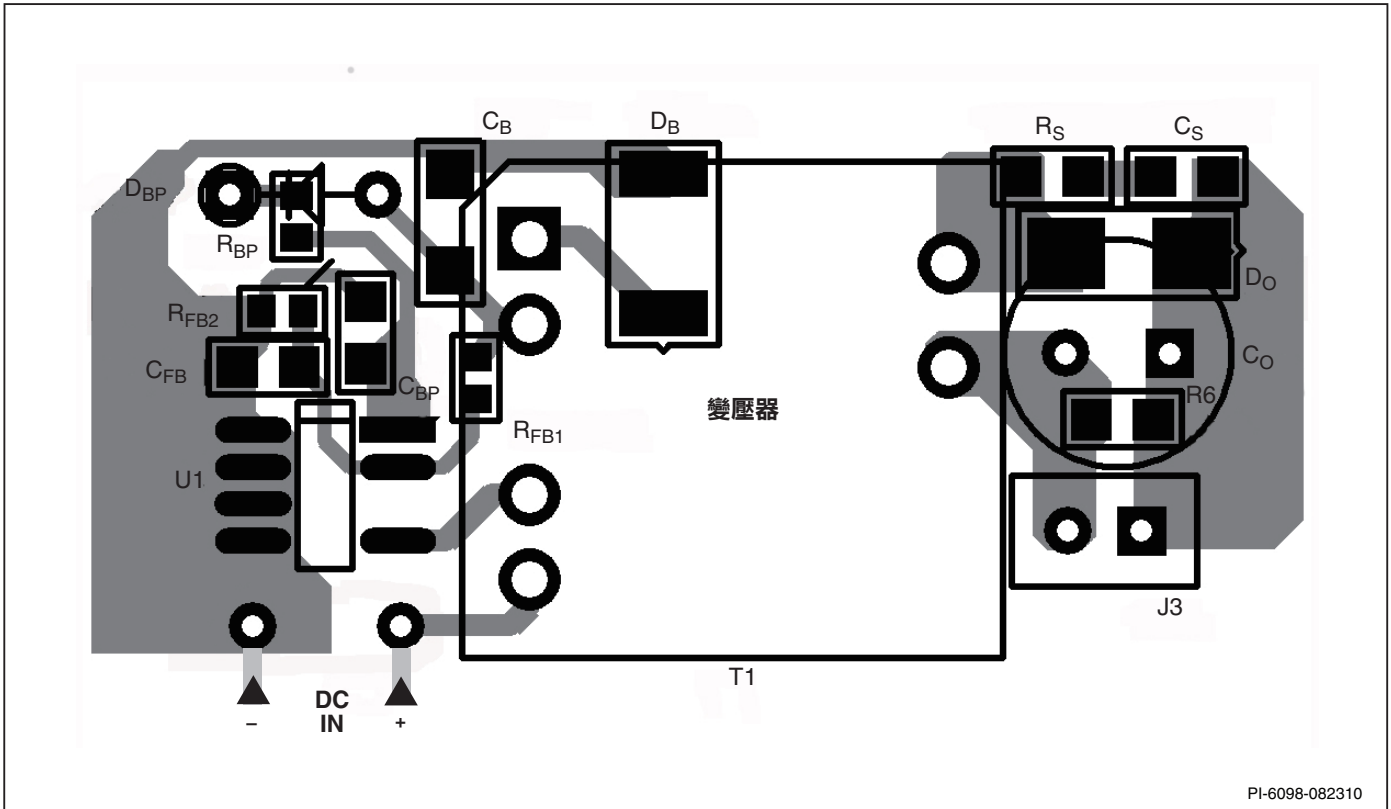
2.1 W、6 V、350 mA 充電器的 PCB 佈局。
